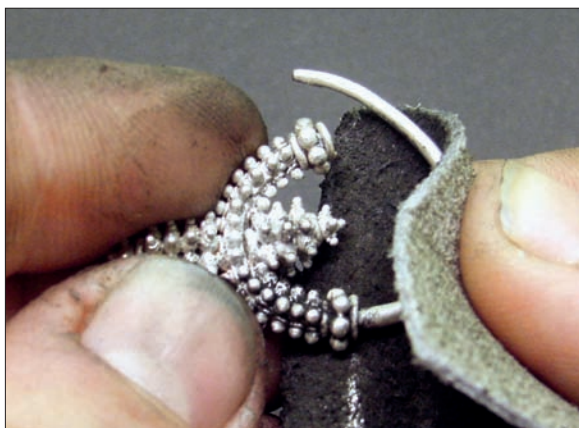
/275: Tělo a hrozníček jsou v místě spoje opatřeny difuzní pájkou.
